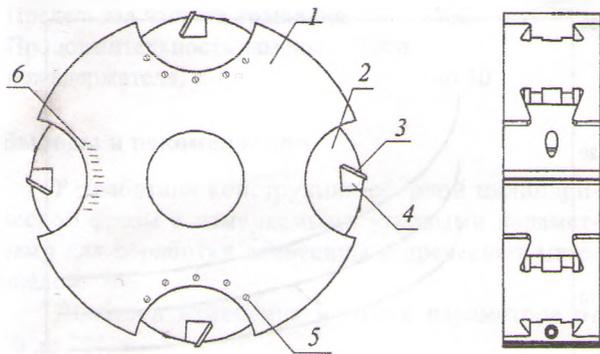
Фреза цилиндрическая с изменяемыми угловыми параметрами: 1 – корпус; 2 – сегменты-ножедержатели; 3 – нож в виде неперетачиваемой пластины; 4 – клин, 5 – винты; 6 – шкала углов резания
